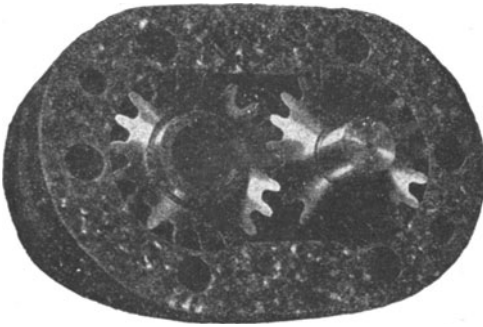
Ölpumpe für die Drühdölschmierung der Dampfturbinenlager.
